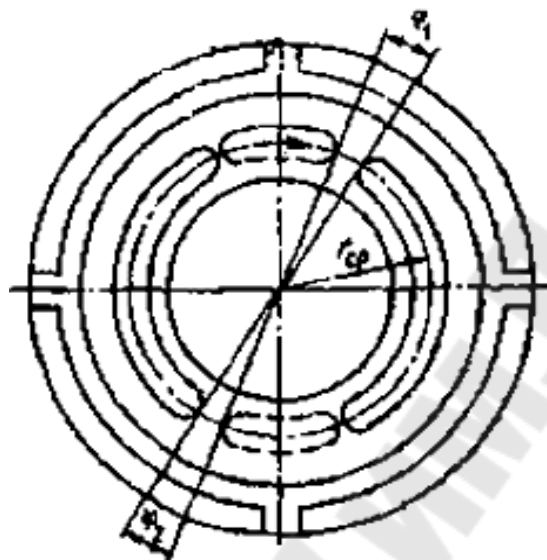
Схема к расчету углов перекрытия торцового распределителя
